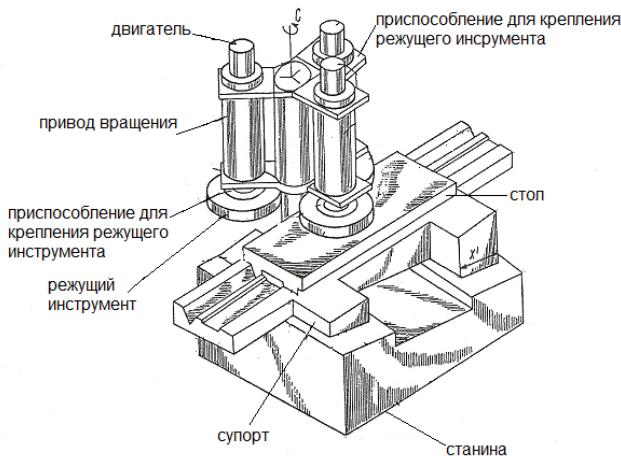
станок для размерного микрошлифования с тремя режущими инструментами
